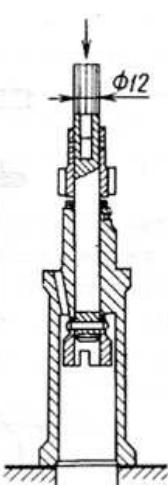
Zalisování ložiska s hřídelíkem vodního čerpadla v tělesu
